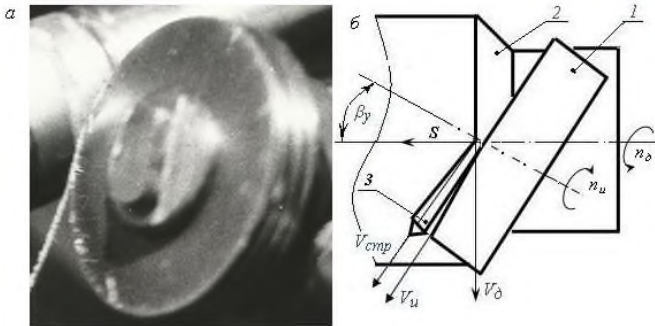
Процесс (а) и схема (б) резания многолезвийным ротационным инструментом: 1 – режущие элементы; 2 – обрабатываемая деталь; 3 – отделяющаяся стружка, β_y - угол установки режущих элементов; ω_d, ω_u - угловая скорость детали и режущих элементов соответственно; V_d, V_u - линейная скорость детали режущих элементов соответственно
